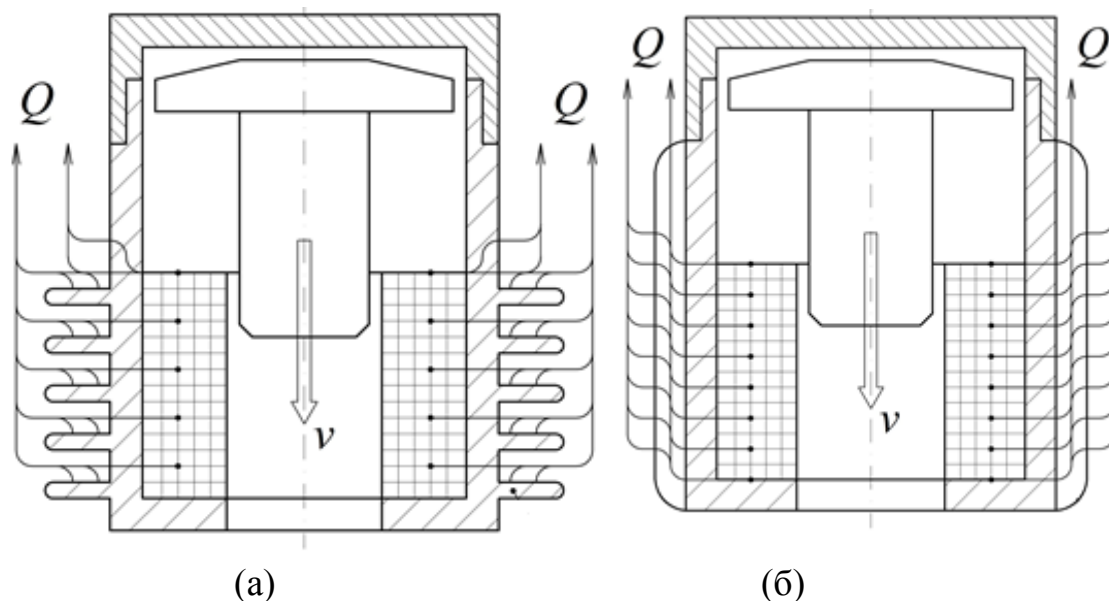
Линейные электромагнитные двигатели с оребренной боковой поверхностью корпуса: с радиальным (а) и осевым (б) расположением охлаждающих ребер.
